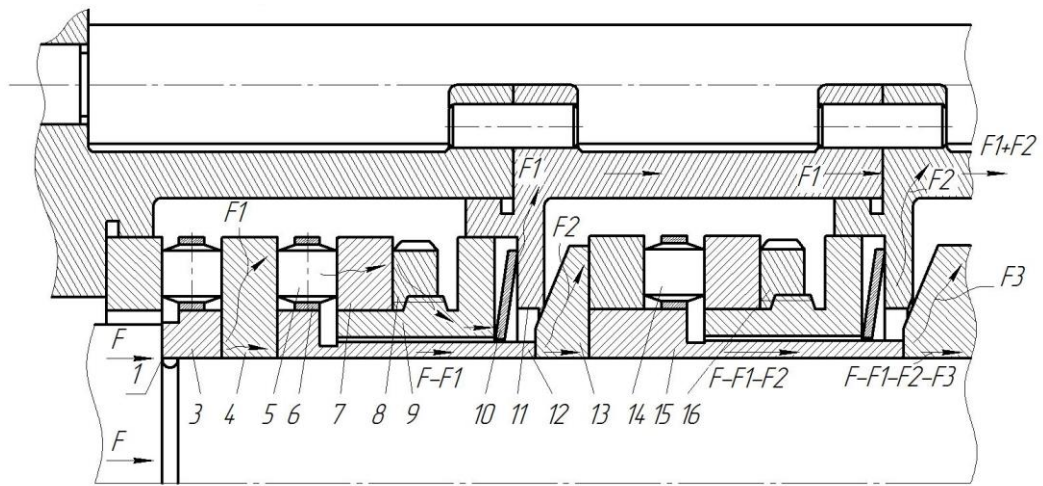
Вузол опорного підшипника двочерв'ячного змішувача:
